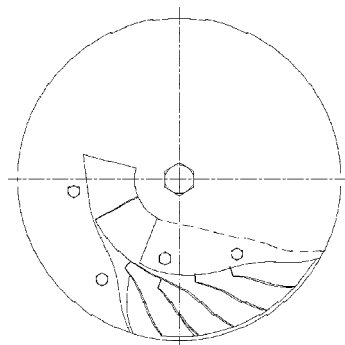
Приспособление для упрочнения сектора моноколеса компрессора
